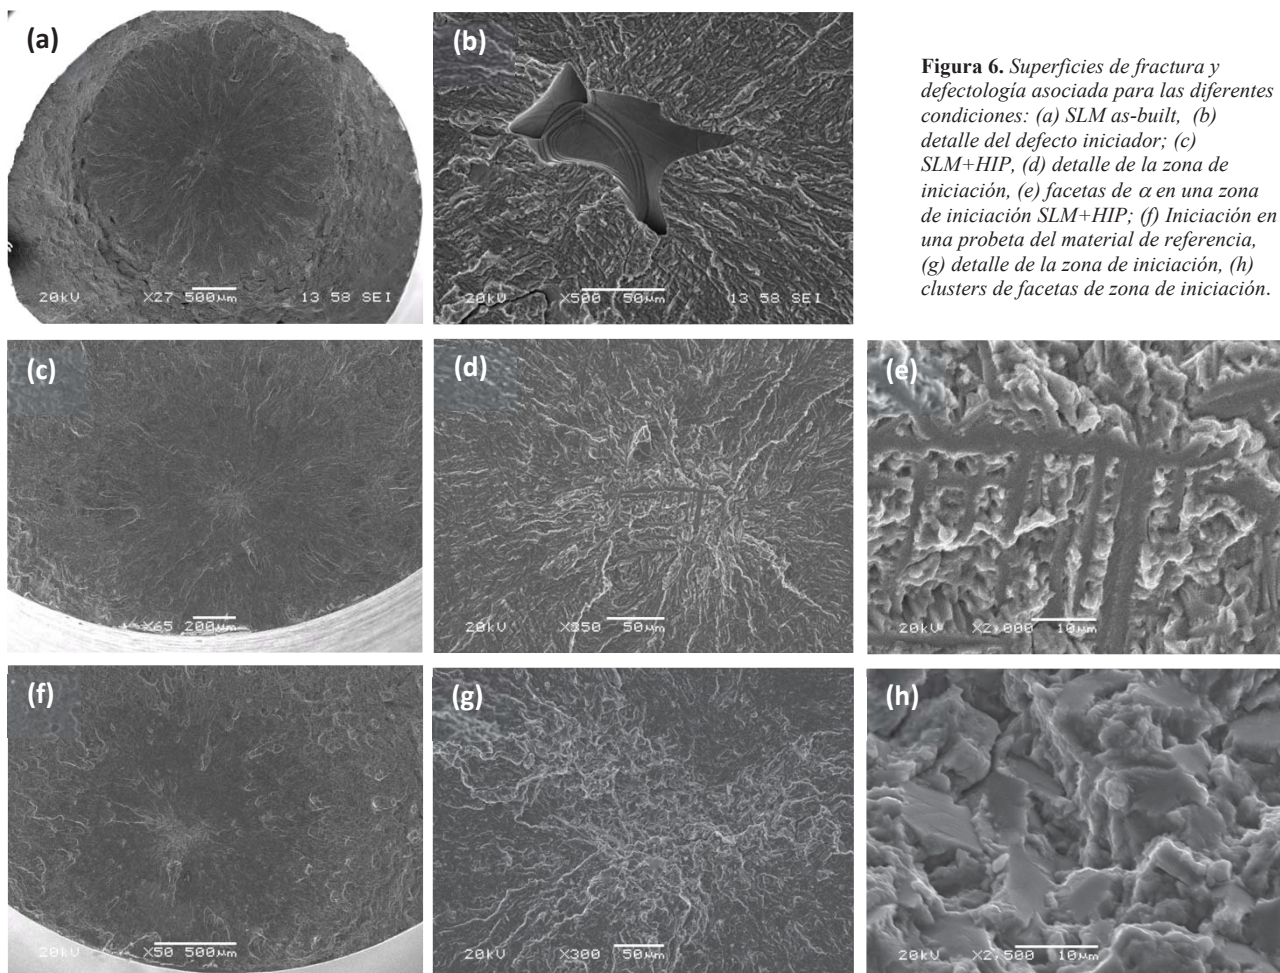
Superficies de fractura y defectología asociada para las diferentes condiciones: (a) SLM as-built, (b) detalle del defecto iniciador; (c) SLM+HIP, (d) detalle de la zona de iniciación, (e) facetas de α en una zona de iniciación SLM+HIP; (f) Iniciación en una probeta del material de referencia, (g) detalle de la zona de iniciación, (h) clusters de facetas de zona de iniciación.
